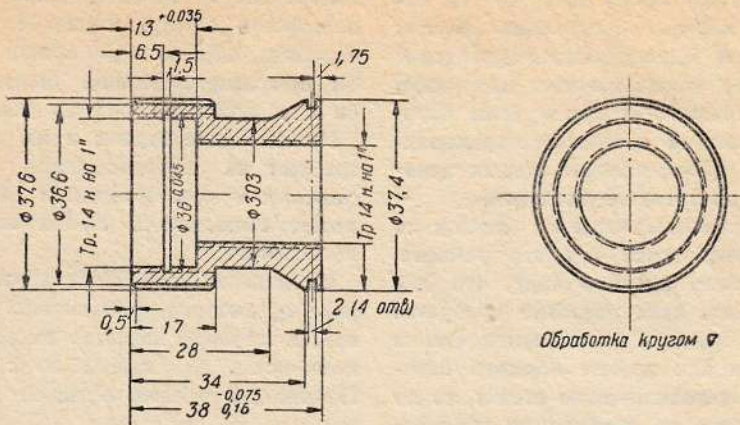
Втулка для шарикоподшипника стабилизатора скорости (со стороны маховика)
